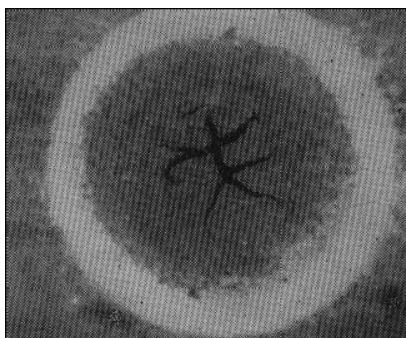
Наружные трещины сварной точки (под увеличением)
